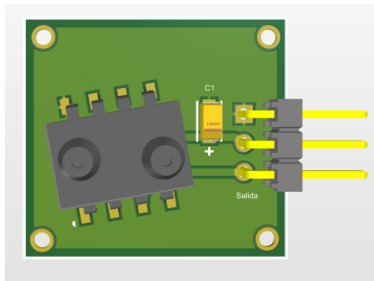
CAD PCB del sensor del segundo prototipo del dispositivo Ubicu.
